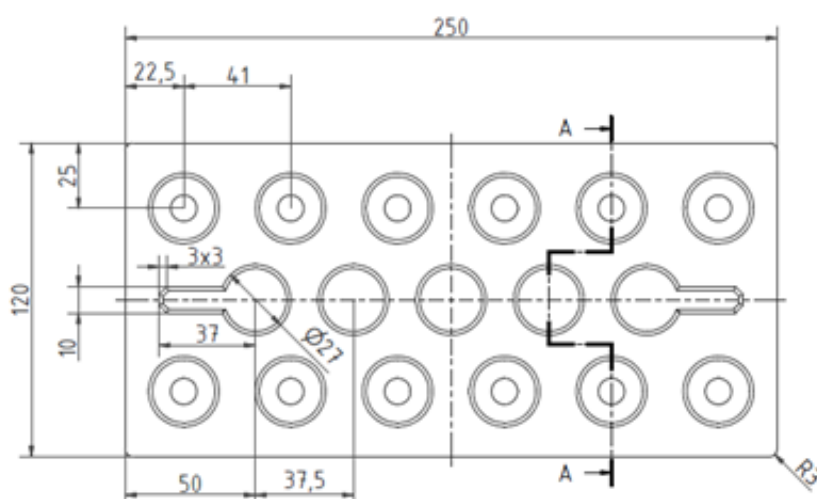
Detalles de la pieza GEROBLOK PERFORADO 50 dBA.
